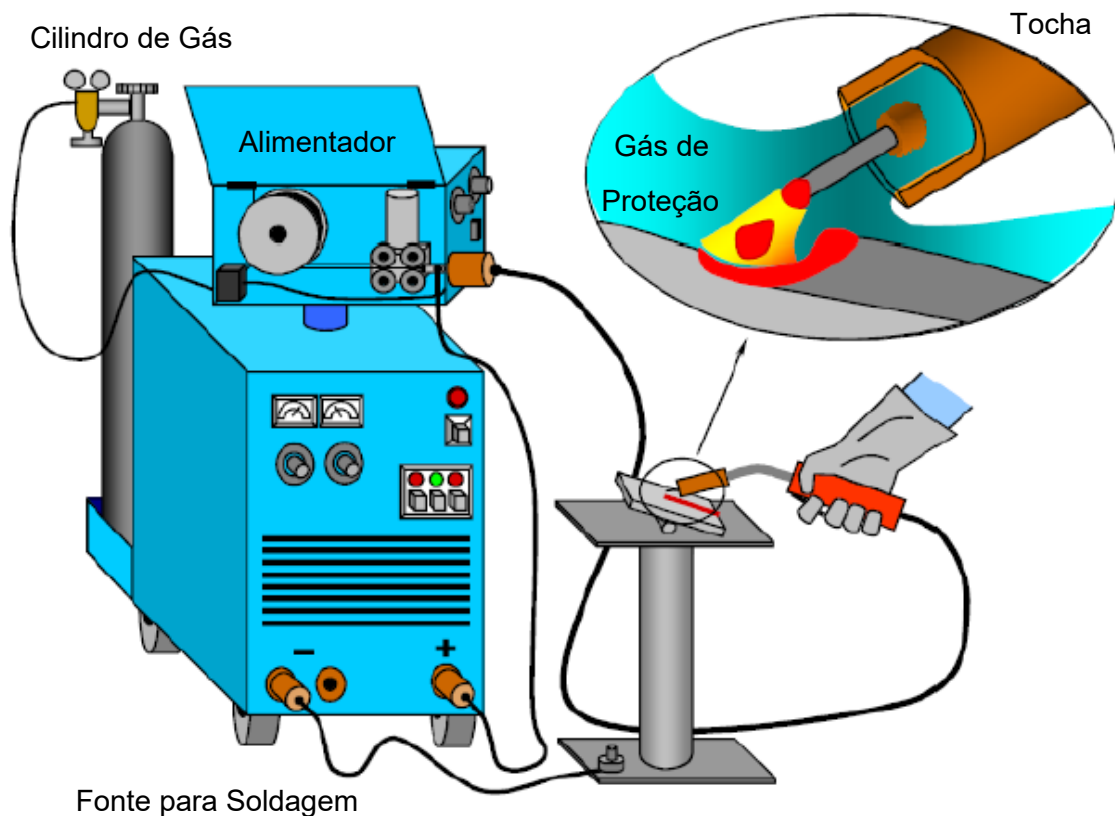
Esquema do processo MIG/MAG. Fonte: Material didático a disciplina de Soldagem e Fundição do Prof.º Dr. Volodymyr Ponomarov
